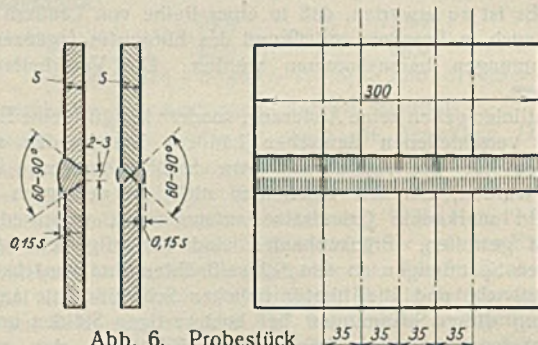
Probestück zur Schweißungsprüfung (Stumpfnähte).
